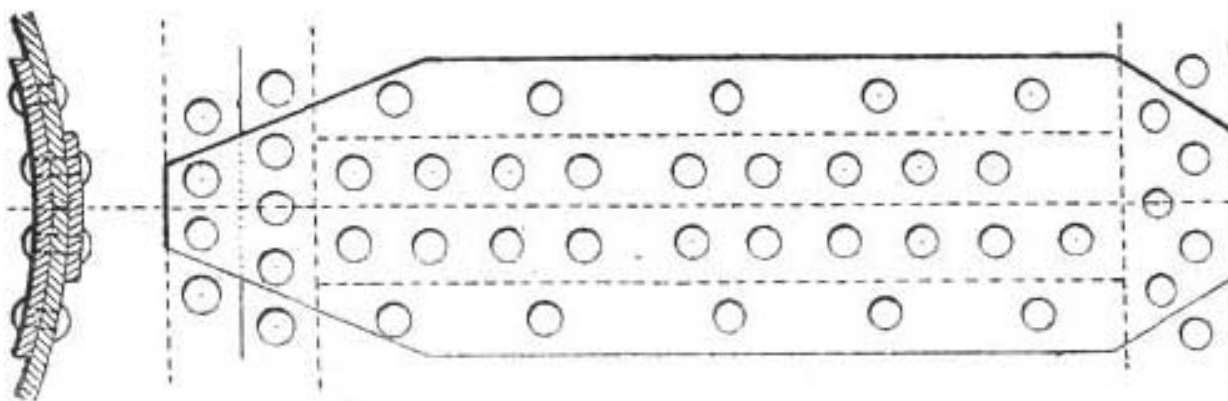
Remachado longitudinal con dos cubrejuntas desiguales. La misma disposición existe con cuatro filas de remaches sobre el cubrejunta exterior y seis filas sobre el cubrejunta interior (fig.157)
